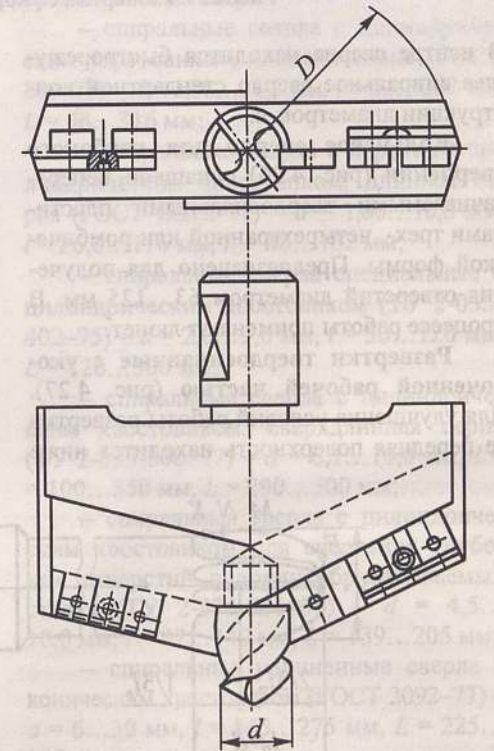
Сверло перовое с неперетачиваемыми пластинами
